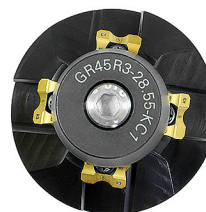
°-Radius-Fräser mit 4 Schneiden und Führungsrolle, bestückt mit 4 x 3 mm-Radius-Wendeschneidplatten vom Typ R-K
